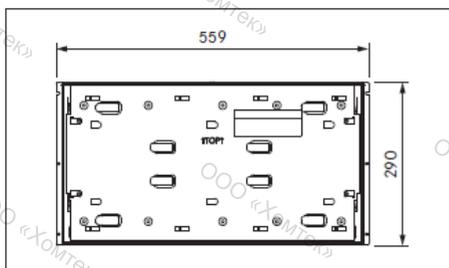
Размеры прибора, модель MS290, вид спереди
